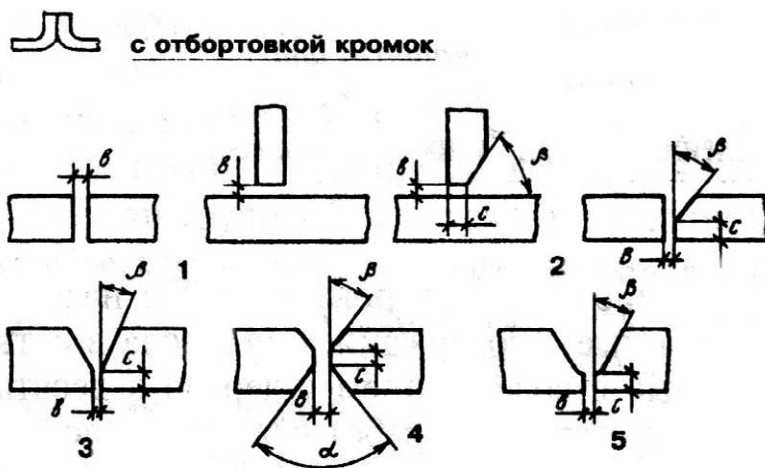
Конструктивные элементы разделок кромок под сварку:
